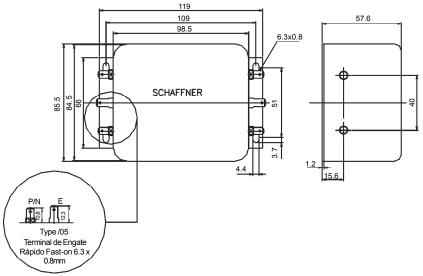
Desenho do filtro externo FS6007-16-06
